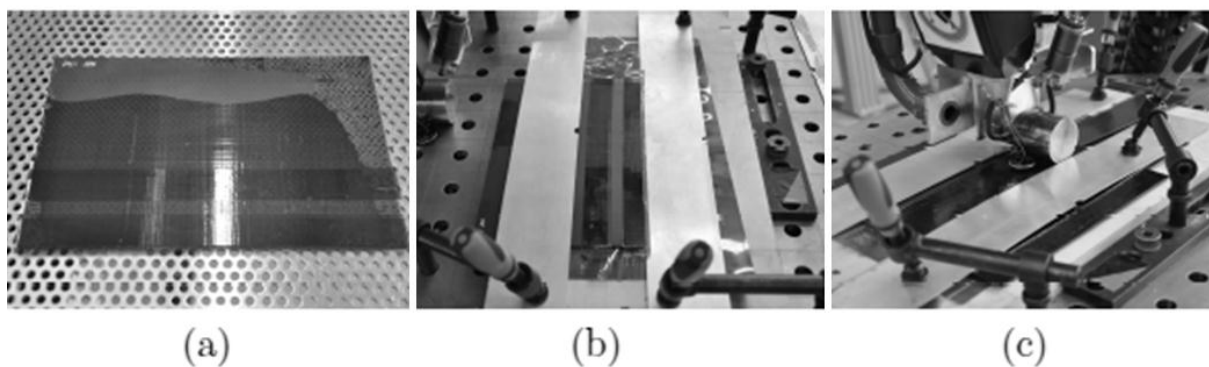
Verschweißung der Single-Lap-Shear-Prüfkörper ((a) Beschränken des Schweißbereichs mit Polyimidklebeband; (b) Einspannen der Prüfplatten vor dem Schweißprozess; (c) Verschweißen der Prüfkörper))
